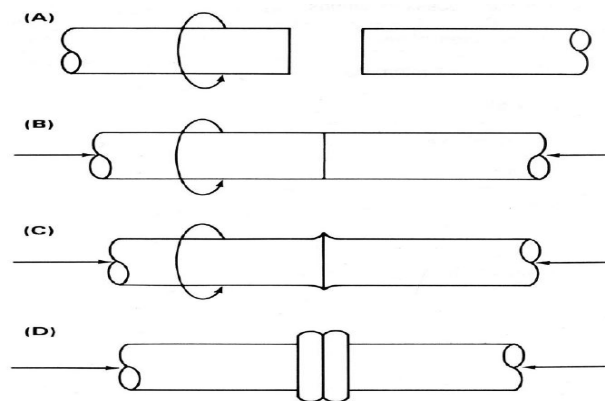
Schéma du procédé de soudage par friction,
